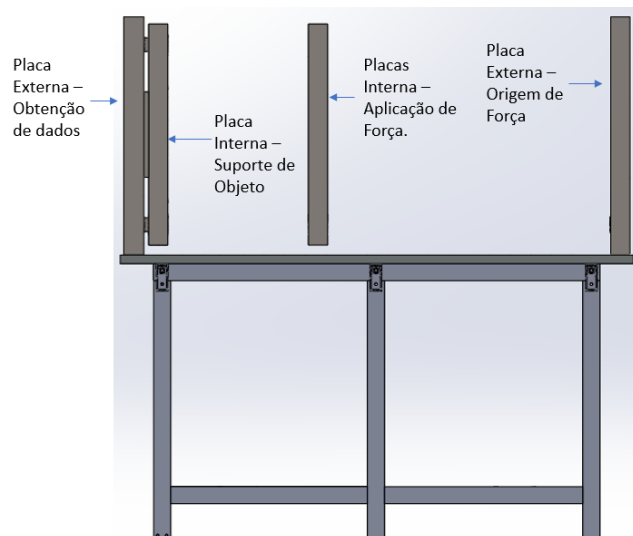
Posição do conjunto de placas que constituem a ferramenta.
